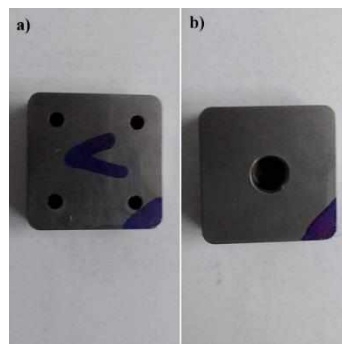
Ferramenta utilizada no torneamento. a) Lado usado com fluido de corte abundante, b) Lado usado com refrigeração interna.
